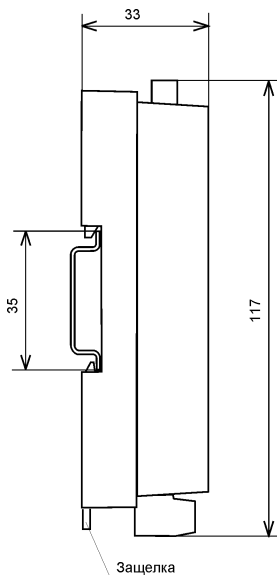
Габаритный чертеж модуля с креплением к DIN-рейке.
